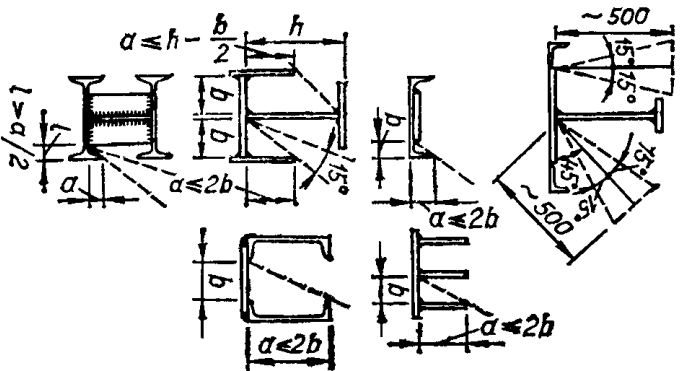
Пределные размеры выступающих деталей при сварке различных конструкций.
